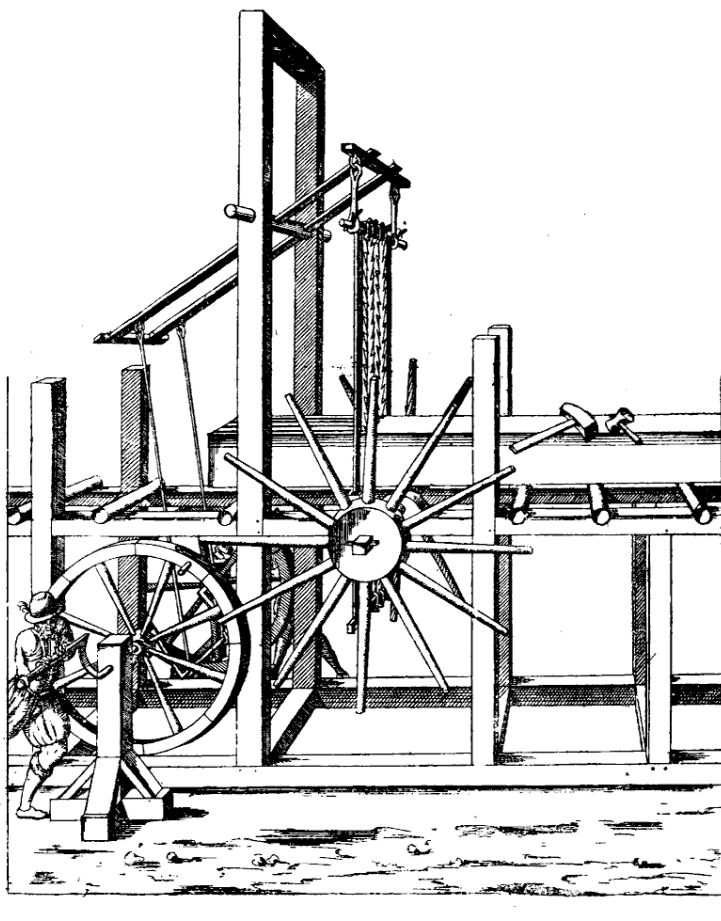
Machine à scier le bois avec avancement automatique (xvi^e siècle) (JACQUES BESSON, 1578).
